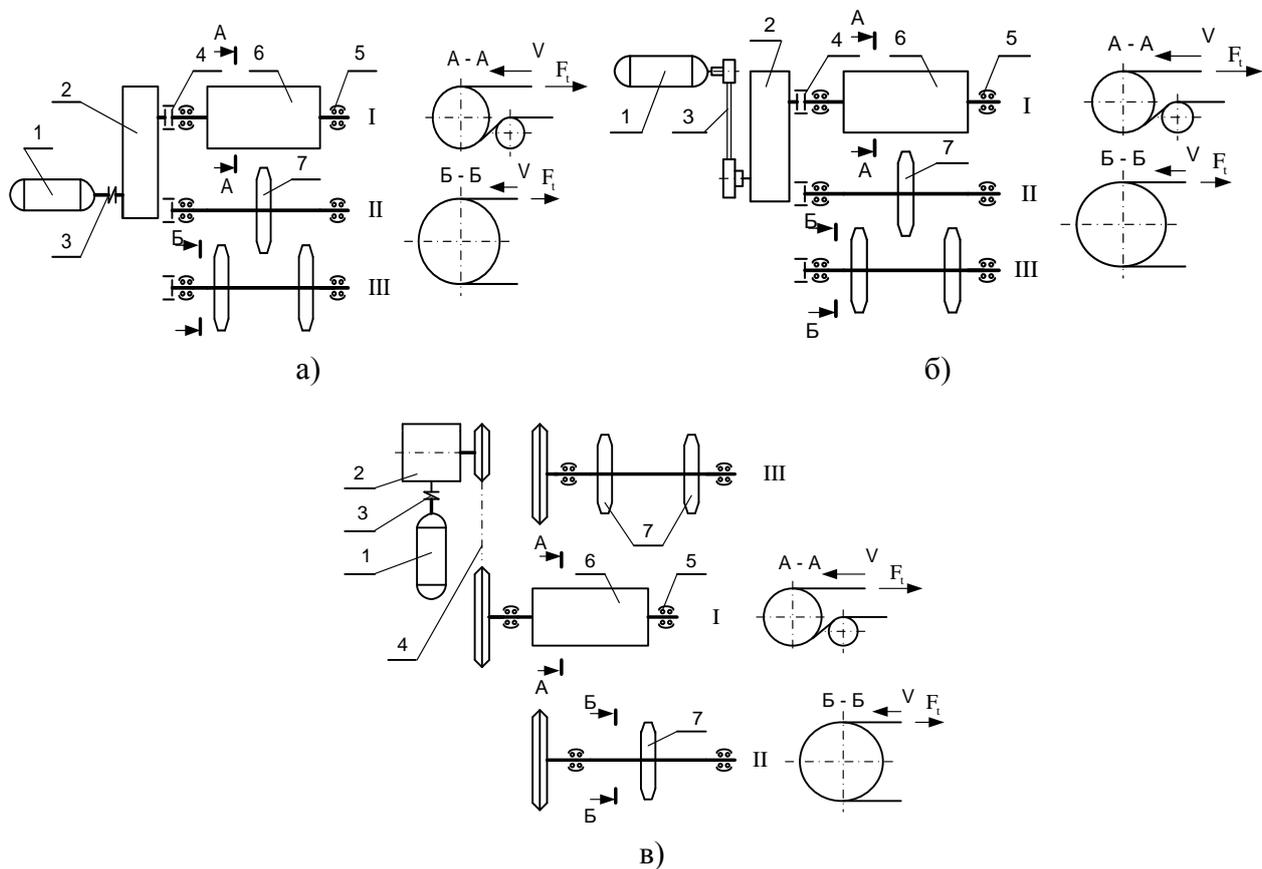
Кинематические схемы приводов конвейеров с передаточным механизмом, включающим: а) редуктор цилиндрический зубчатый; б) редуктор цилиндрический зубчатый и ременную передачу; в) редуктор червячный и цепную передачу
